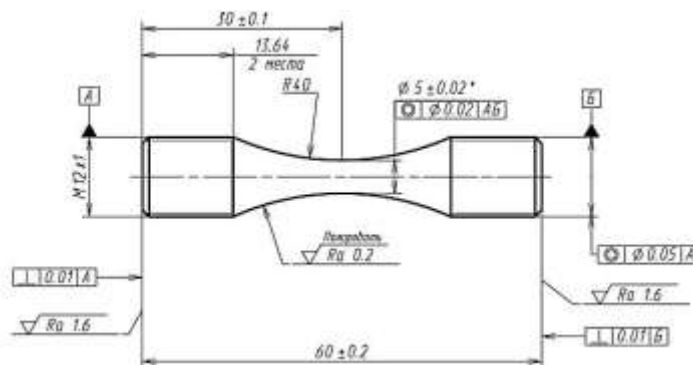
Гладкий цилиндрический образец с рабочей частью переменного сечения для испытаний по схеме нагружения «растяжение-сжатие»
